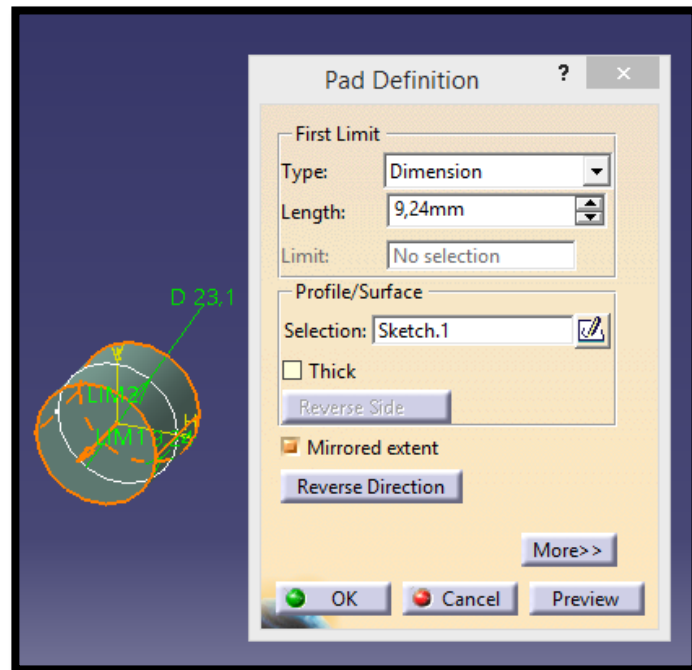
Seat mounting frame 11: Pad brazo oscilante inferior
